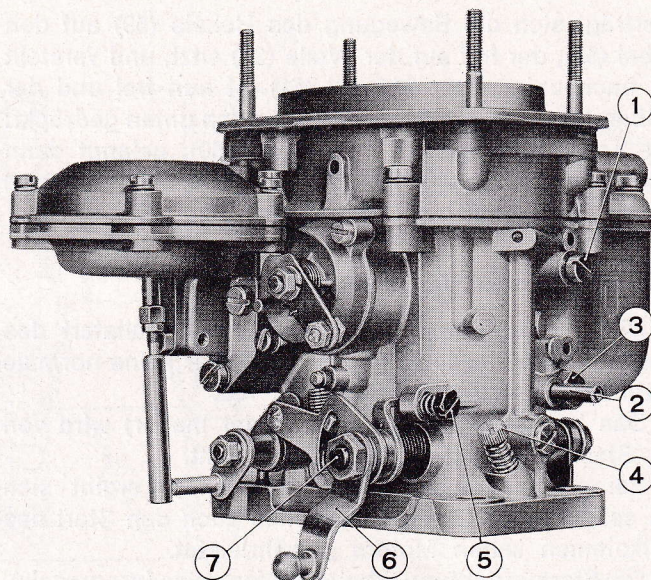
Weber-Vergaser 34 DCHD 4, für Motor 115 C.005.
